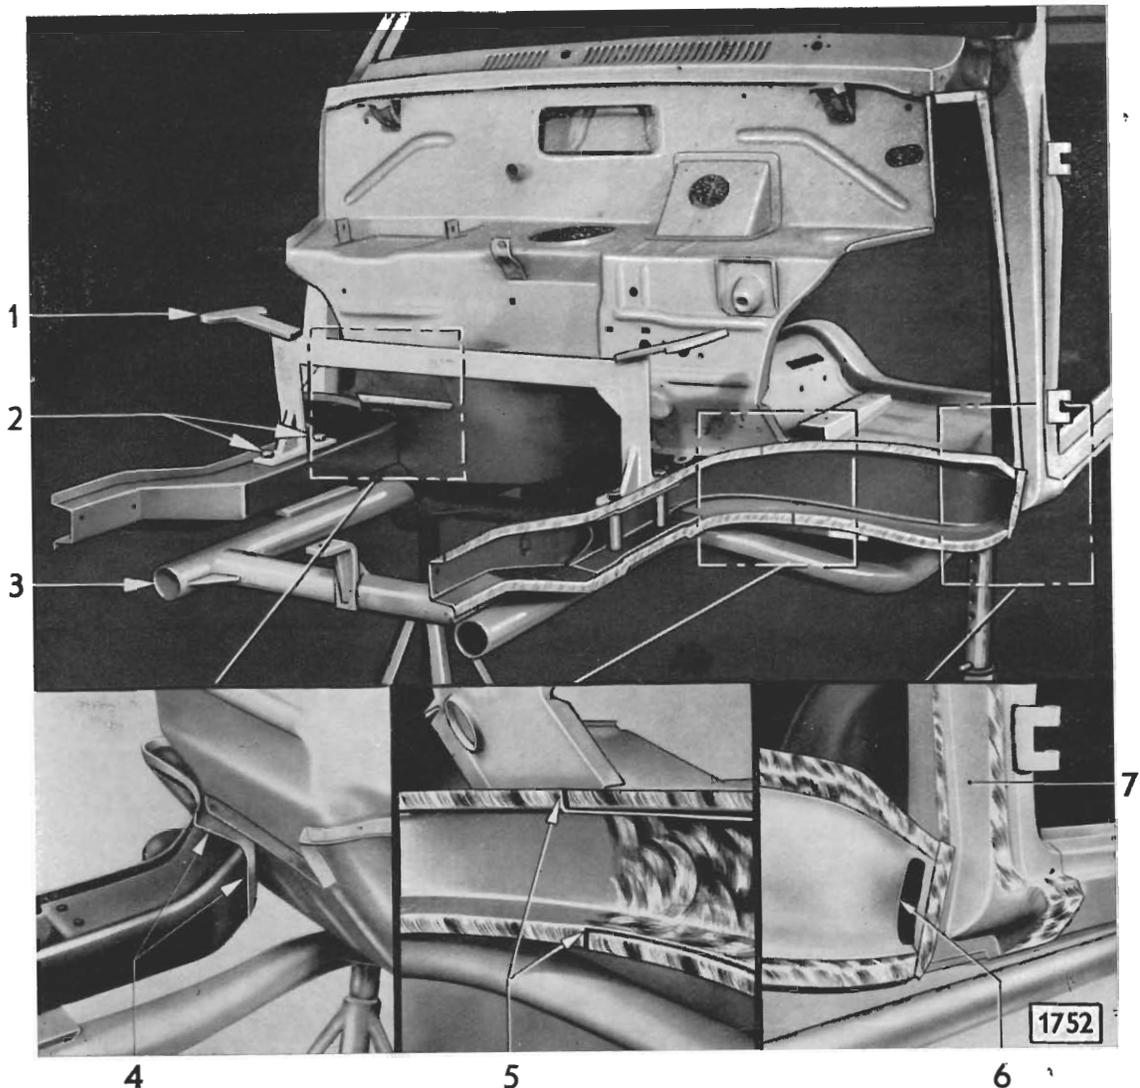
Linken Vorderrahmenlängsträger in Längsträgerrest gelegt und mit Vorderrahmen-Schweißblehre in Einbaulage gebracht – rechten Längsträger in gleicher Weise in Einbaulage bringen
